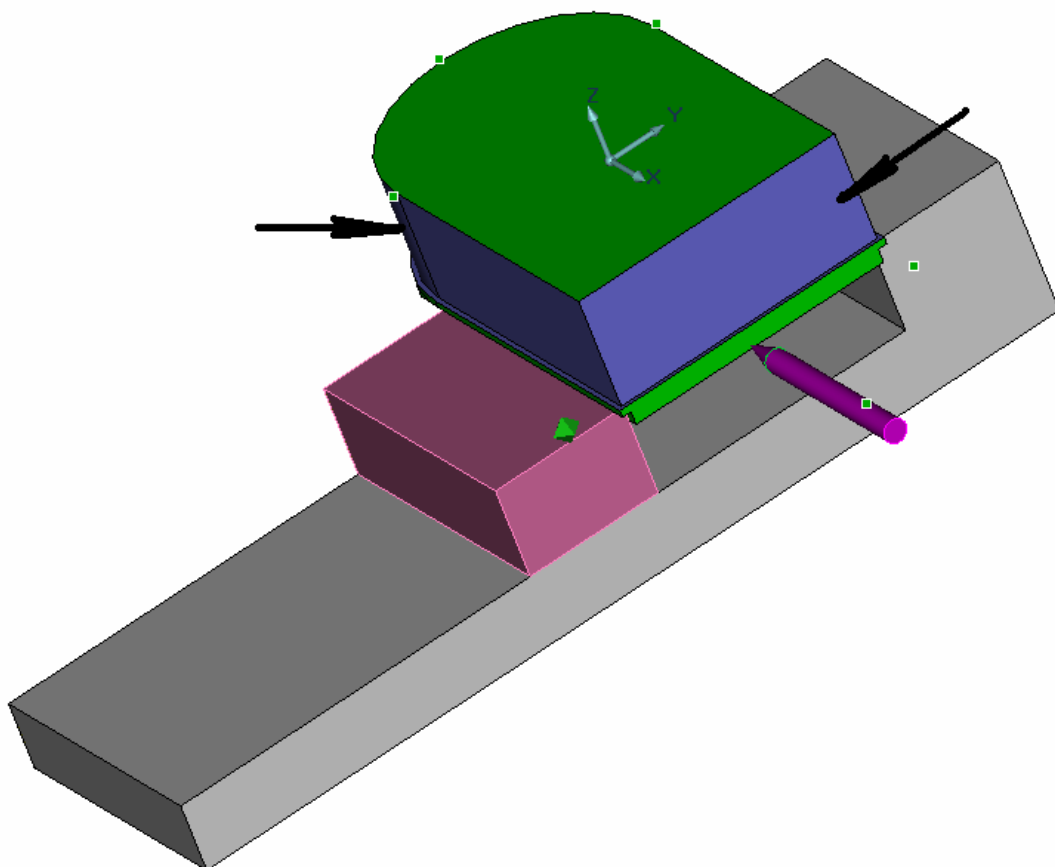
Переход 2 на установке «А»: выполнение полного профиля боковой поверхности
